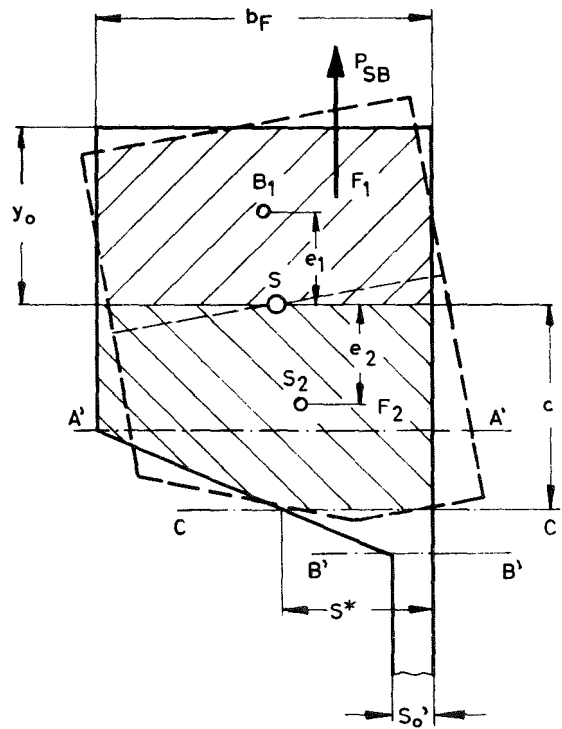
Drehung des Flanschrings um den Schwerpunkt
